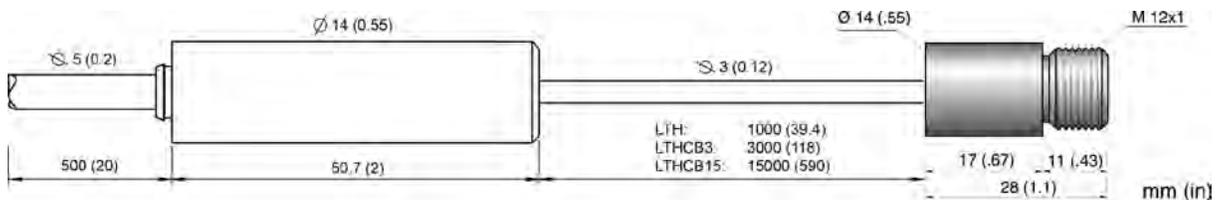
Dimensions de la tête de mesure LTH et Électronique
